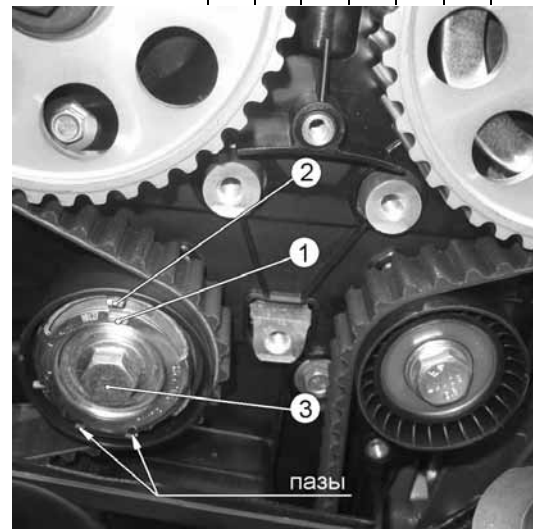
а – Проверка натяжения ремня привода ГРМ 16-клапанного двигателя
